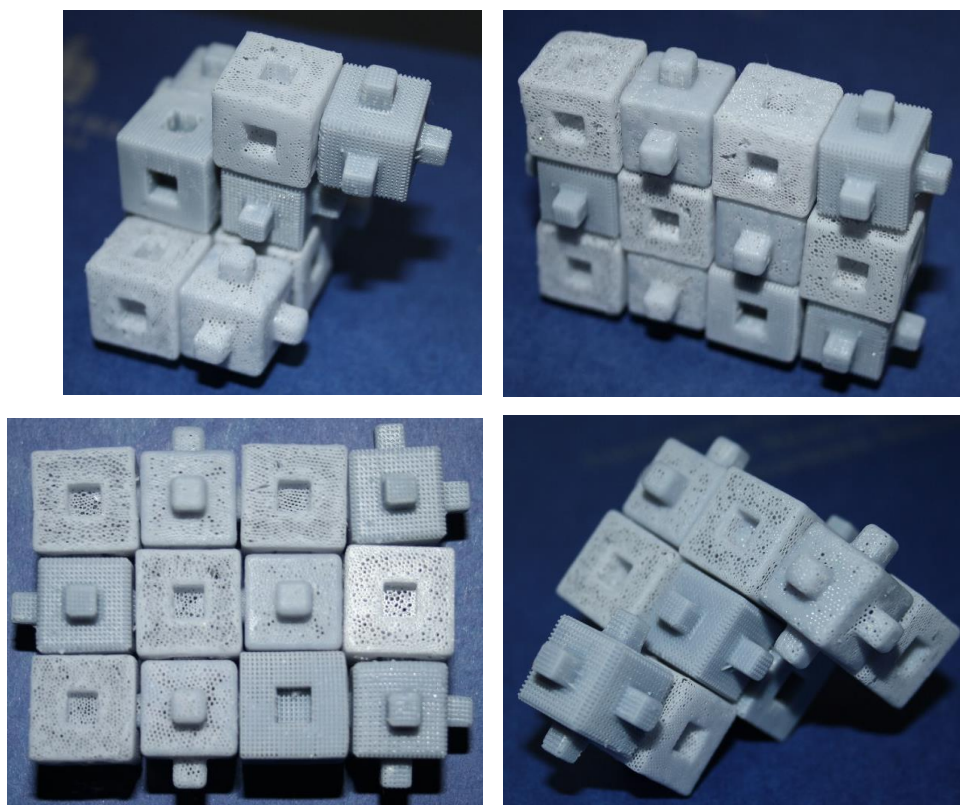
Acoplamiento conjunto de todas las parejas de piezas estructurales
